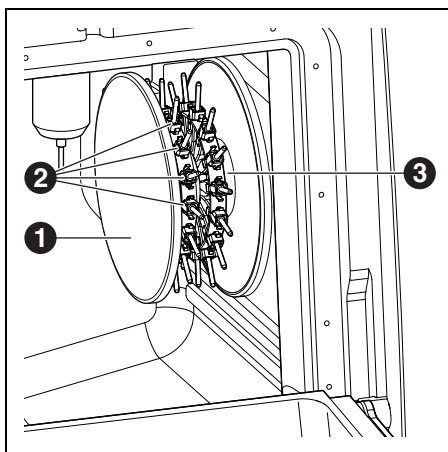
Vista generale supporto utensile (Tool Blank) estratto
